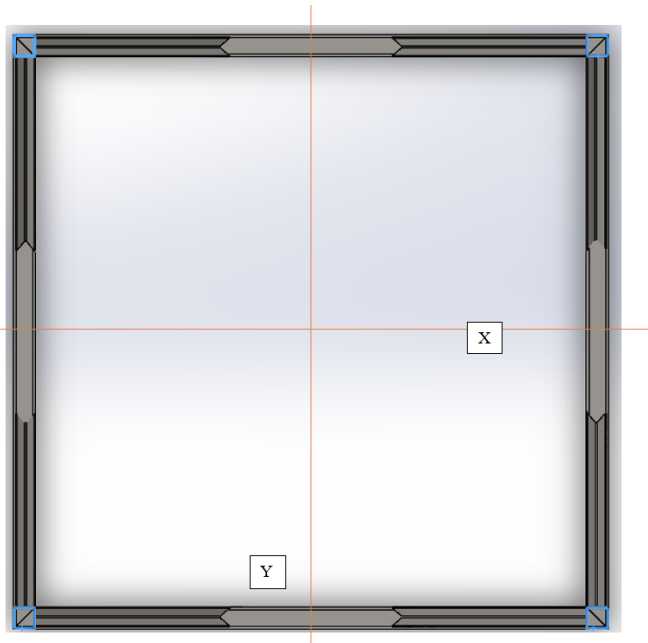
Distribución de vigas verticales en estructura de tolva.
